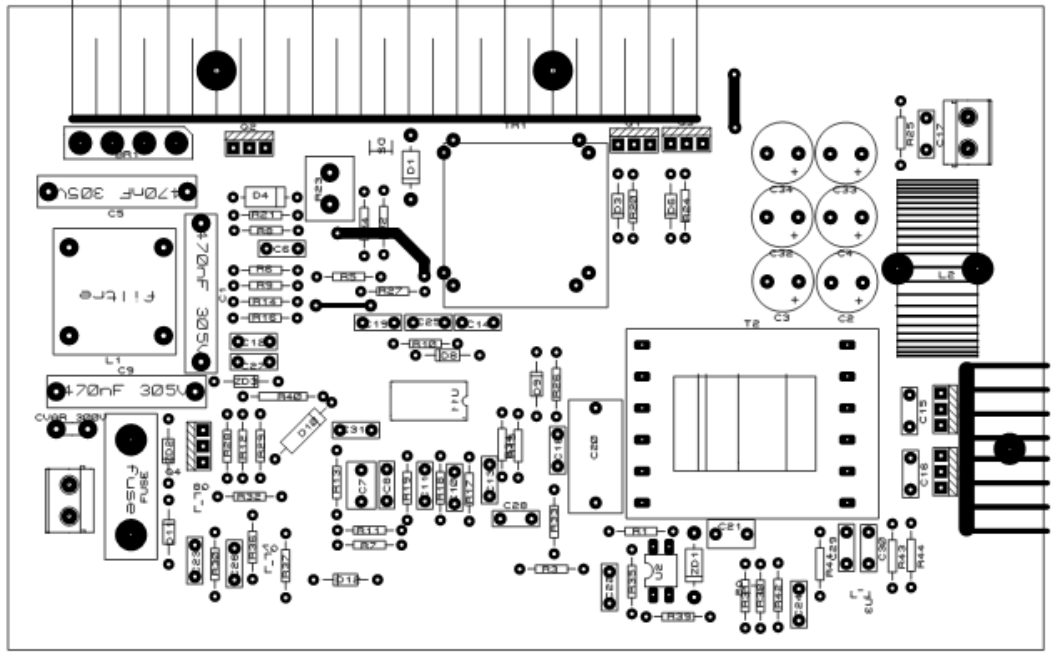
0-30 Volt – 0-3Amper ayarlı güç kaynağı devresi pcb elamanlı yüz
